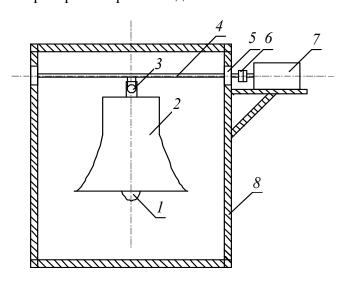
Схема механической части электропривода чаши колокола: I – язык колокола; 2 – чаша колокола; 3 – штанга; 4 – рама; 5 – подшипник; 6 – муфта; 7 – электродвигатель; 8 – станина
